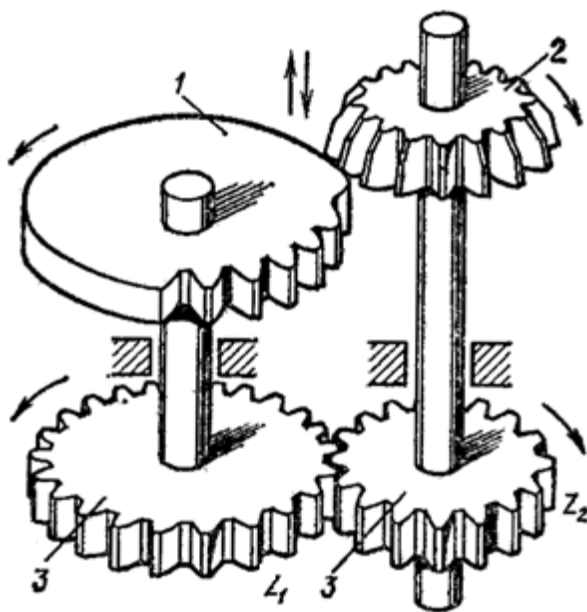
Схема зацепления долбяка с заготовкой при зубодолблении:
